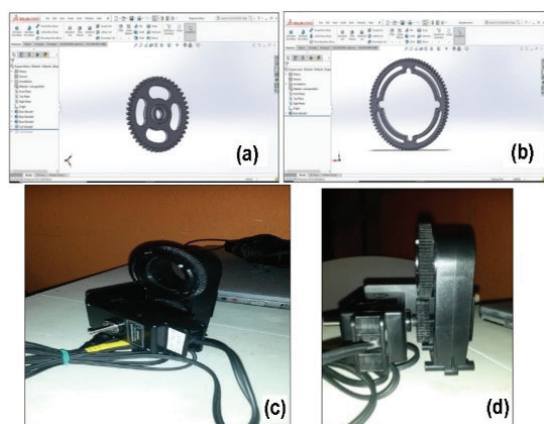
Diseño e implementación de los engranes: (a) y (b) diseño; (c) y (d) impresión en 3D
